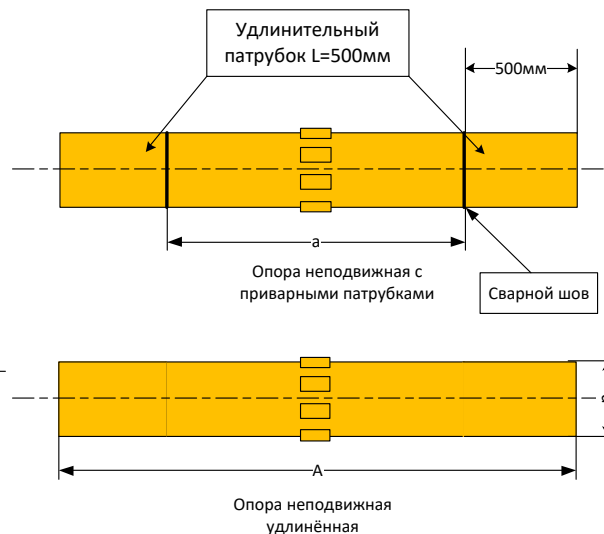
опора неподвижная с приварными патрубками
